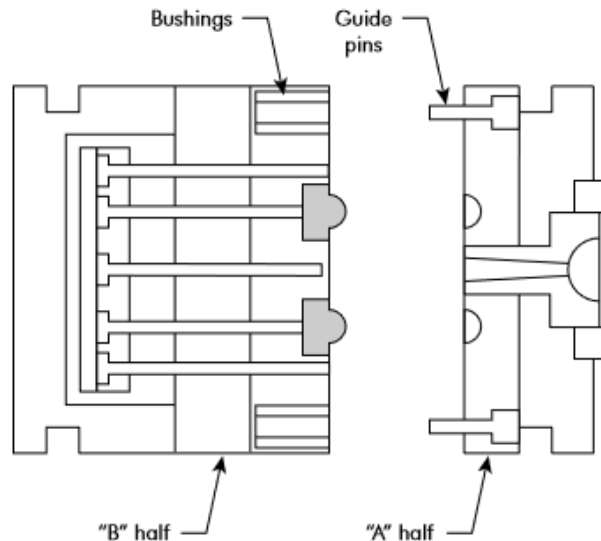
Partes constituintes de um Molde (extraído de Bryce, 1998)
